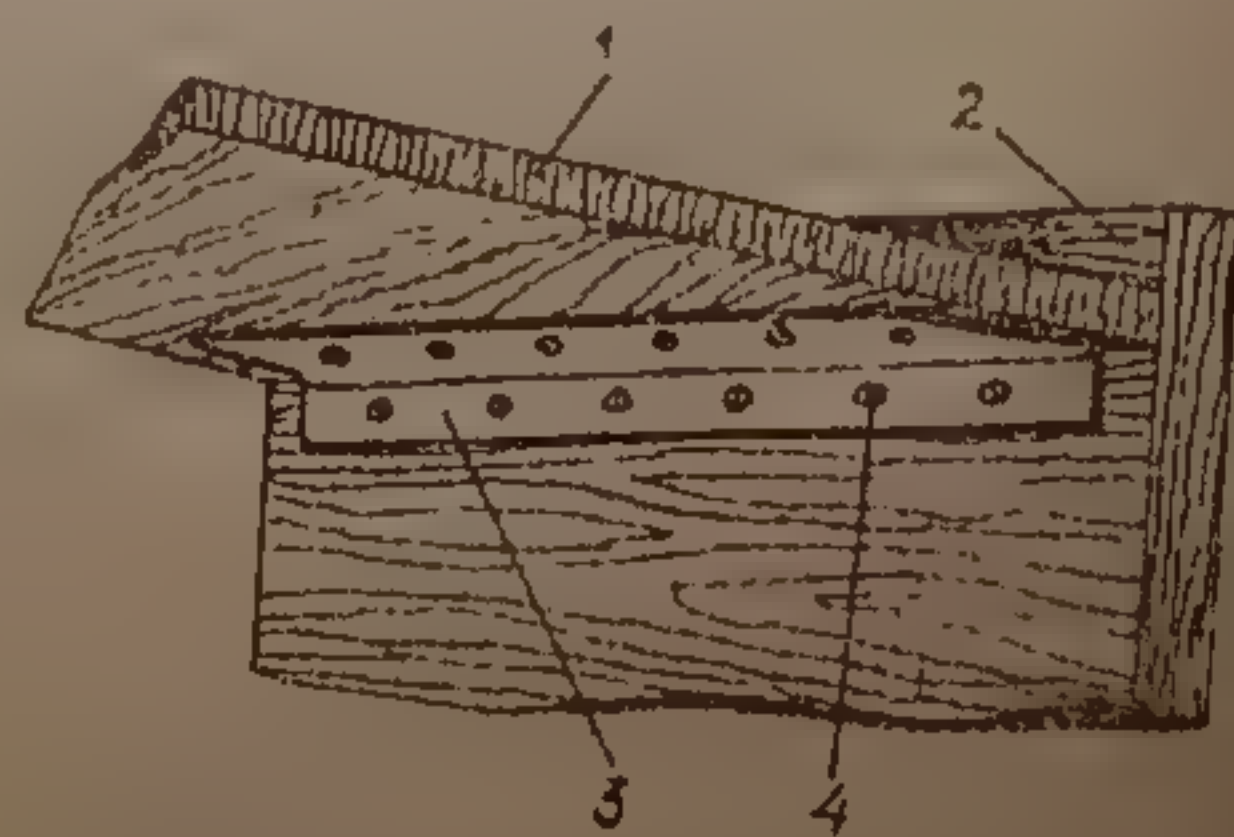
Крепление крышки стола с опорной боковиной: 1 — столешница; 2 — опорная боковина; 3 — металлический уголок; 4 — шурупы
